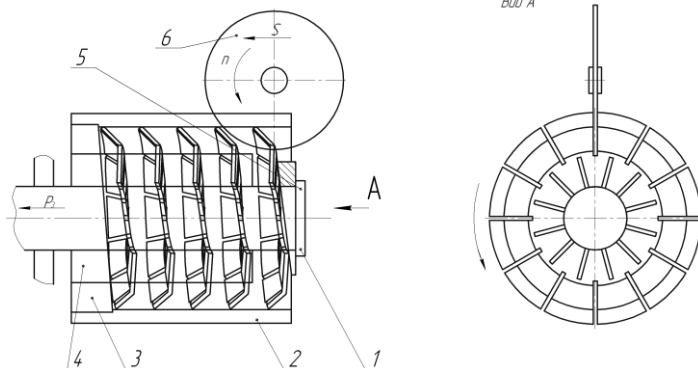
Оправка для розрізання пазів на зовнішньому контурі пружини: 1 – шток; 2 – оправка; 3 – упор; 4 – шпонка; 5 – швидкозмінна шайба; 6 – абразивний дисковий круг
